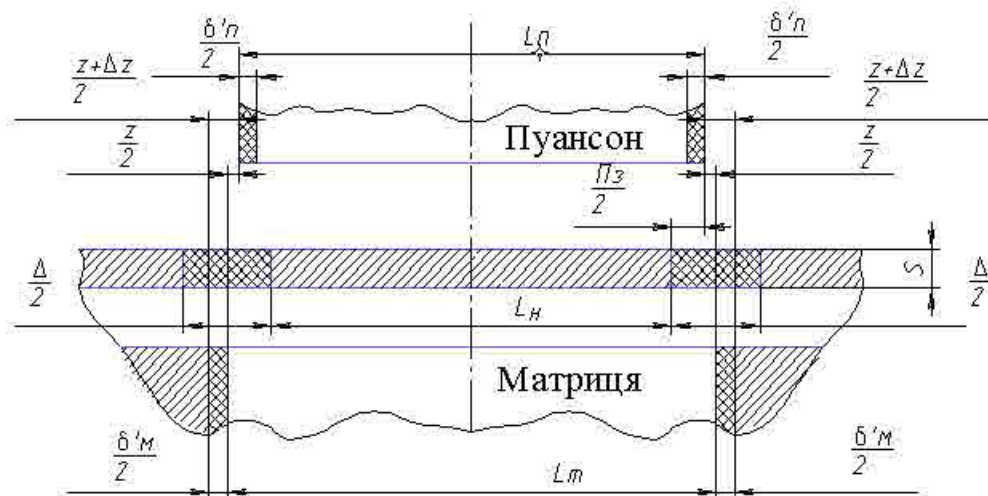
Схема розмірів і полей допусків елемента, що штампується і робочих деталей штампа при їх роздільному виготовленні для операції пробивання отвору: L_n – номінальний розмір елемента, що штампується; L_m – номінальний розмір пуансона; Δ – допуск розміра елемента, що штампується; Π_n – припуск на знос пуансона і матриці; δ_n і δ_m – допуски розмірів пуансона і матриці; z і Δz – зазор і поле допуску зазора між матрицею і пуансоном.
